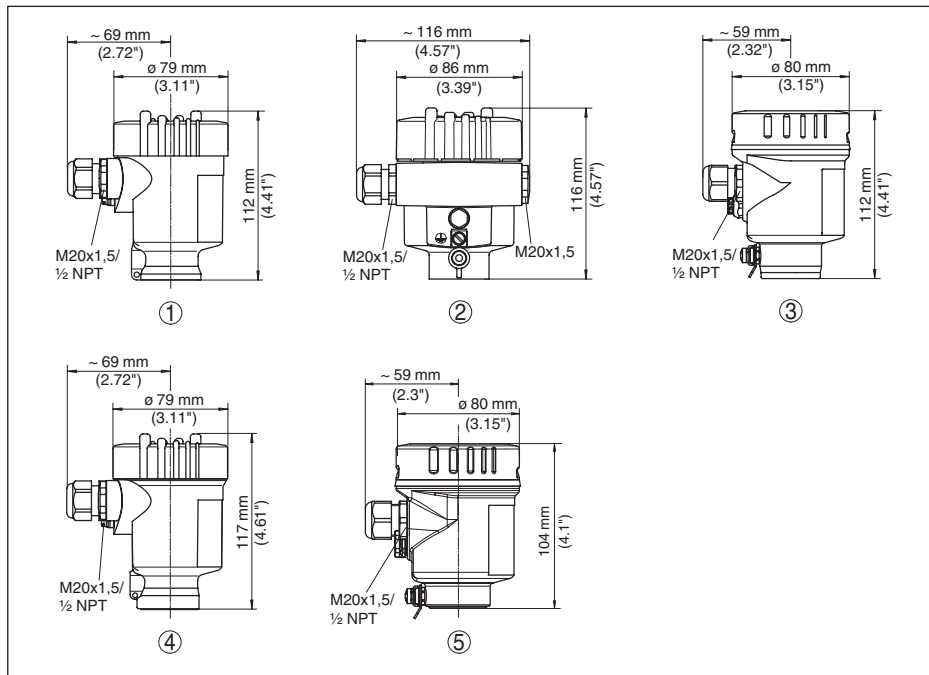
Исполнения корпуса со степенью защиты IP 66/67 и IP 66/68 (0,2 bar)
